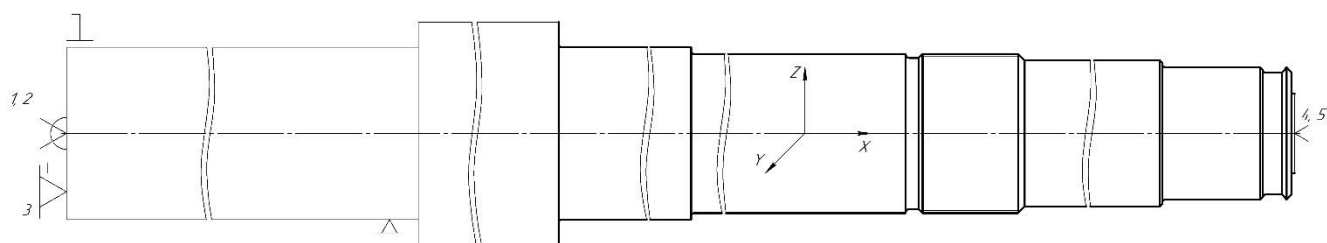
Схема базування заготовки на операції токарній з ЧПК 030, установ А
